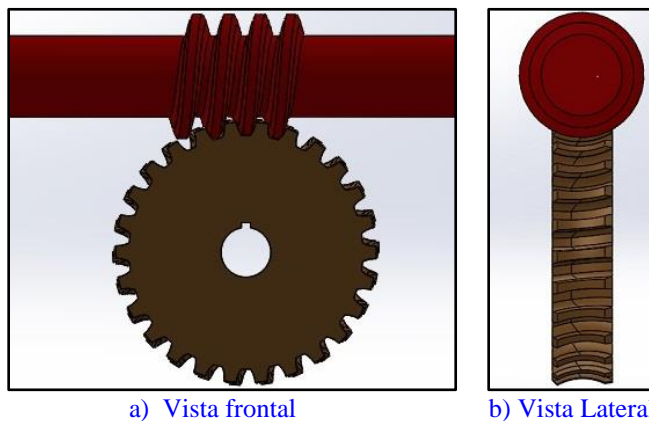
Dibujo en SolidWorks del tornillo sinfín con corona
